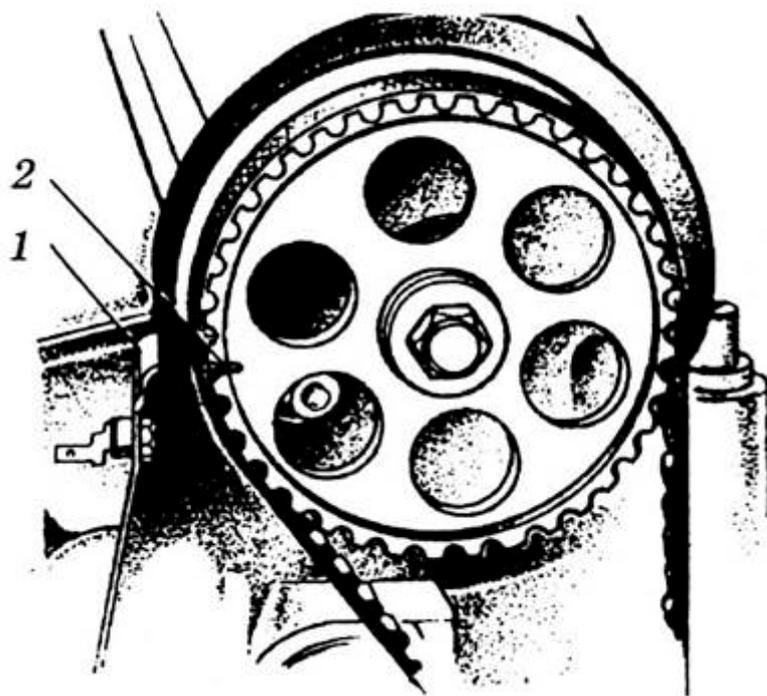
Проверка совпадения меток на звездочке распределительного вала и корпусе подшипников:
